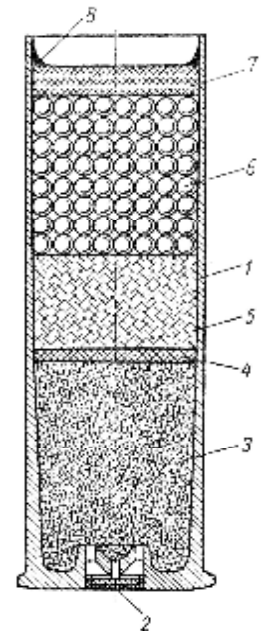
Дробовой патрон, снаряженный в металлическую гильзу (по А.И. Толстопяту). 1 — гильза; 2 — капсюль; 3 — пороховой заряд; 4 — картонная прокладка; 5 — войлочный пыж; 6 — снаряд дроби; 7 — дробовой пыж; 8 — закрепление дробового пыжа путем заливки воском или парафином.
